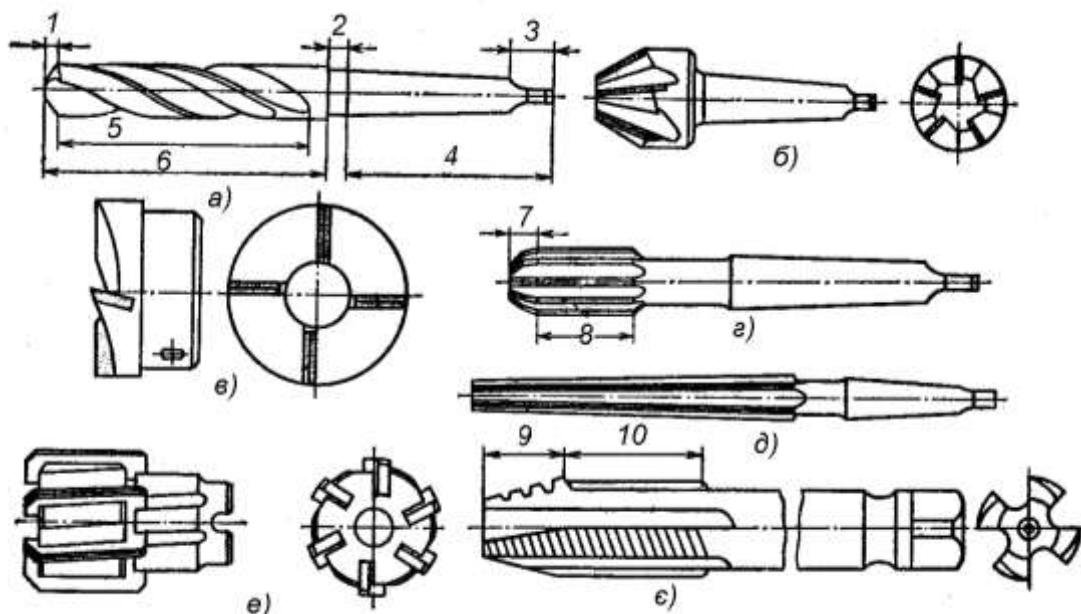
Інструменти для обробки отворів на свердлильних верстах:
